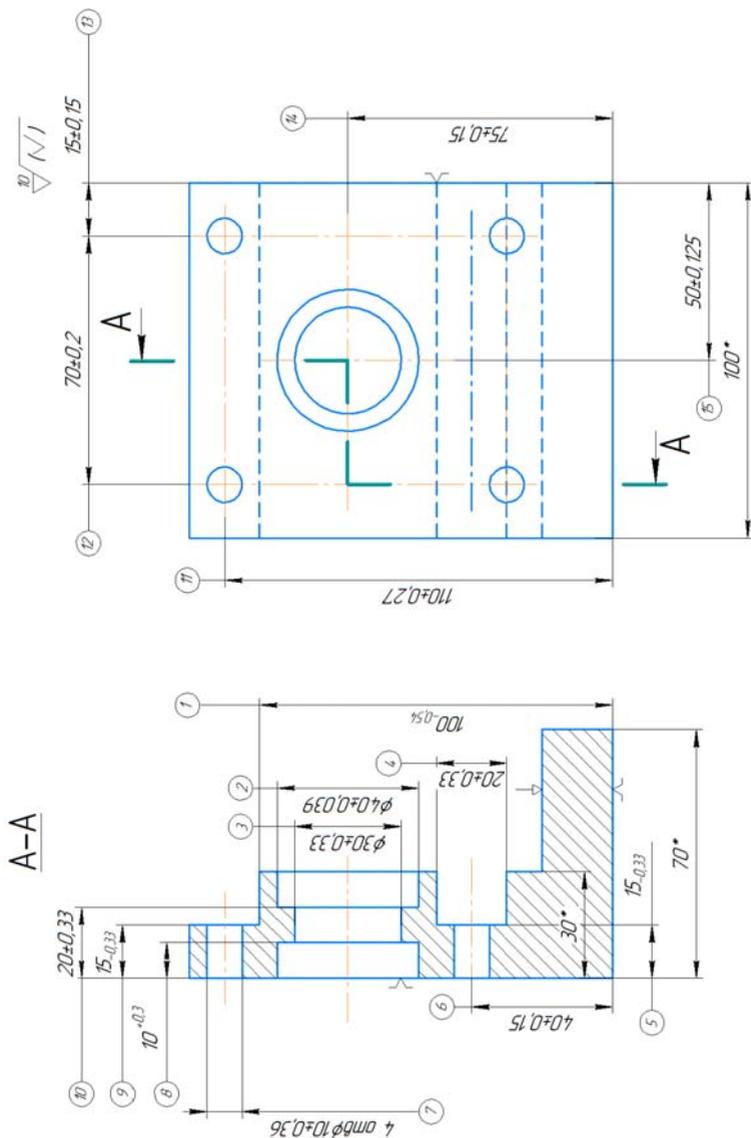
Эскизы заготовки из стали 20 и комплексной операции обработки детали «Стойка» на станке модели ИР500ПМФ4
